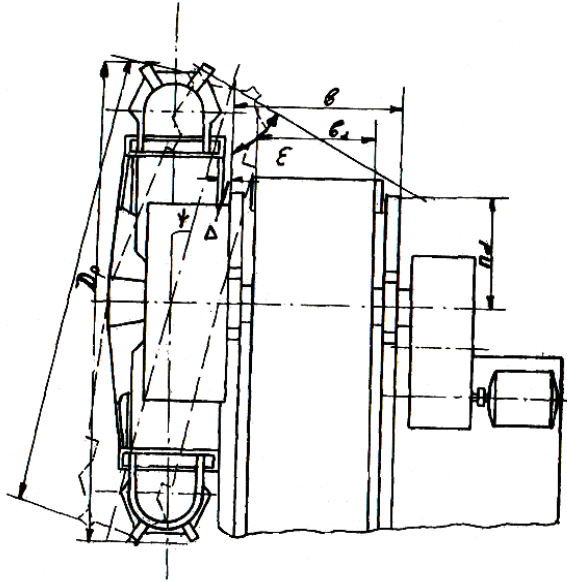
Розрахункова схема для визначення діаметра ротора
